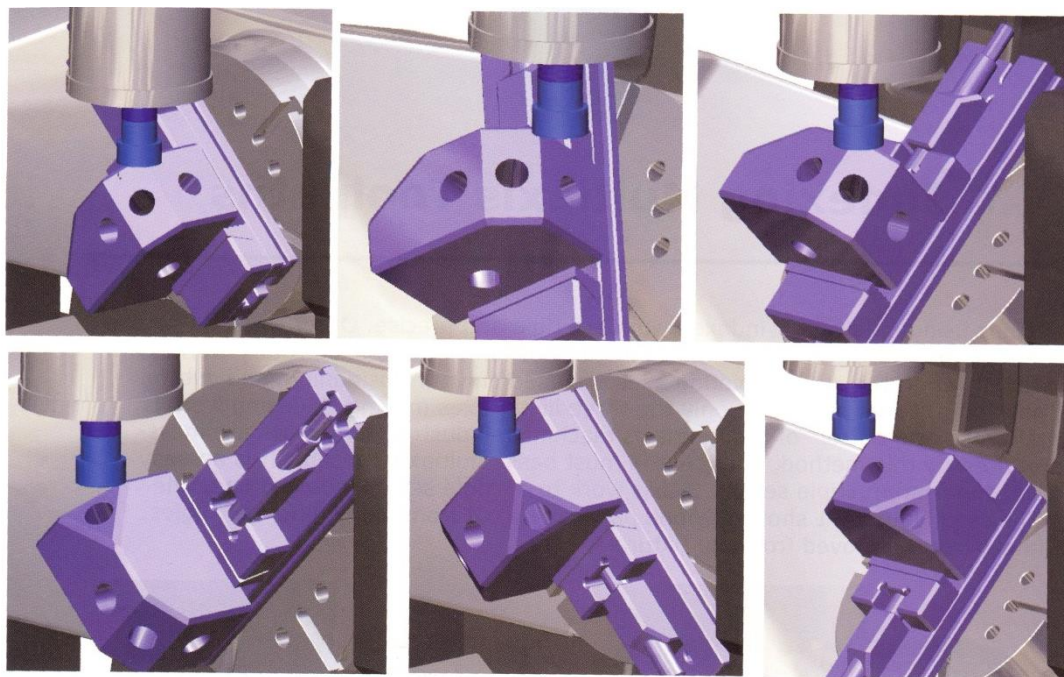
Obrábění součástí na portálovém hlava-hlava obráběcím stroji, kombinace abrazivní vodní paprsek/frézování [16]
